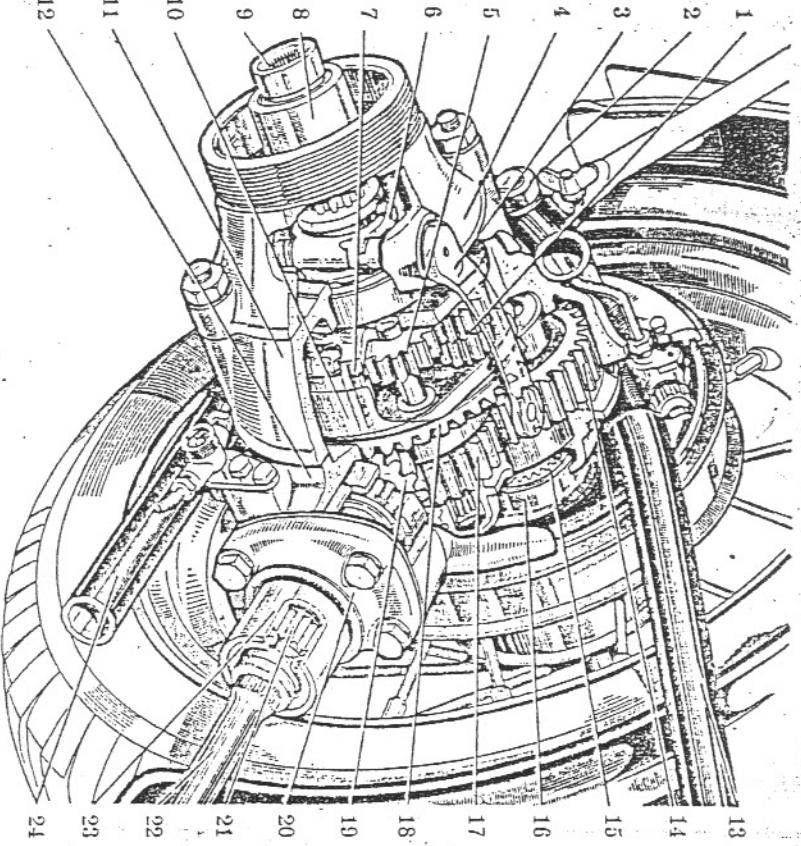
Radauftrieb mit Ausgleichsgetriebe
